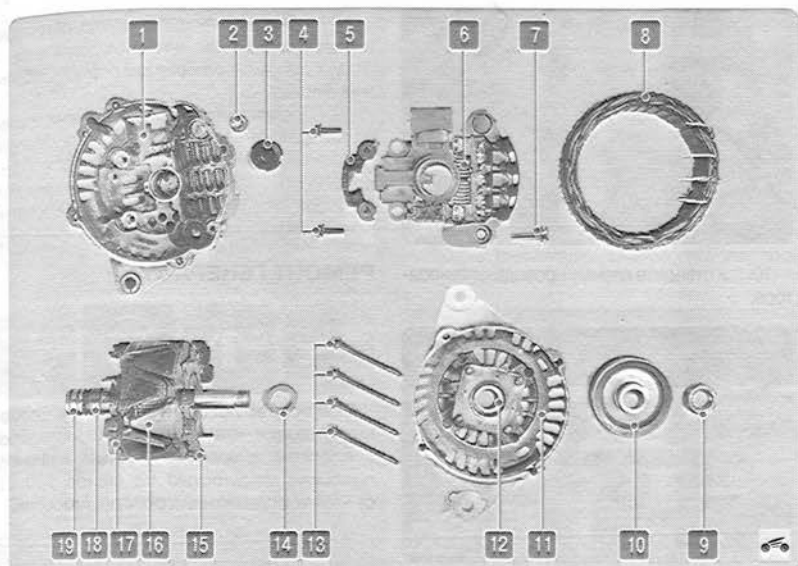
Детали генератора: 1 – задняя крышка; 2 – уплотнительная втулка контактного болта; 3 – гайка контактного болта; 4 – винты крепления прижимной пластины; 5 – прижимная пластина блока щеточного узла и регулятора напряжения; 6 – щеткодержатель в сборе с выпрямительным блоком и регулятором напряжения; 7 – болт крепления щеточного узла; 8 – статор; 9 – передняя крышка генератора; 10 – передний подшипник; 11 – гайка крепления шкива; 12 – шкив; 13 – стяжные болты генератора; 14 – уплотнительная прокладка задней крышки; 15, 17 – крыльчатки вентилятора ротора; 16 – ротор; 18 – контактные кольца; 19 – задний подшипник ротора
